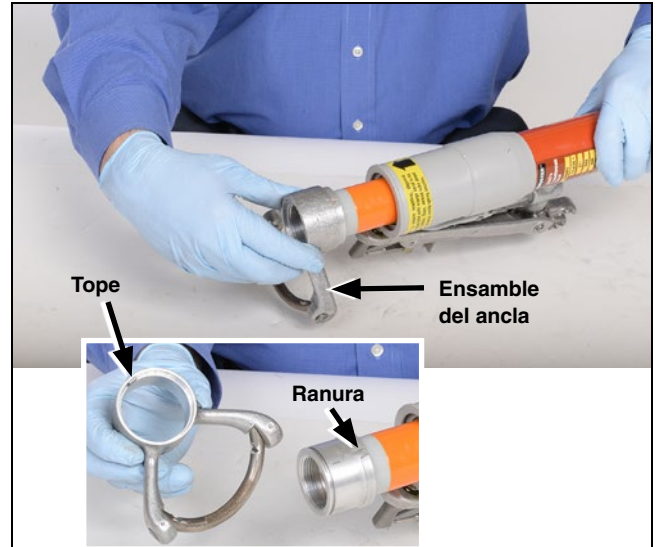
Instale el ensamble del ancla de manera que el tope encaje con la ranura en el ensamble del tubo interno.
